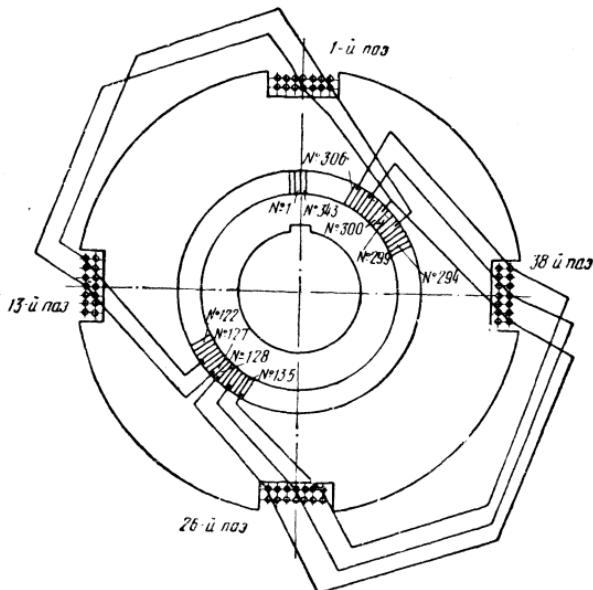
Схема соединения обмотки якоря с коллекторными пластинами двигателя НБ-430А
